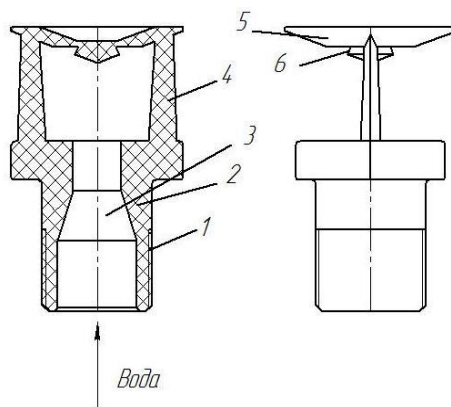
Предлагаемая дождевальная дефлекторная насадка: 1 – резьба; 2 – корпус; 3 – сопло; 4 – ножка дефлектора; 5 – дефлектор; 6 – канавка
